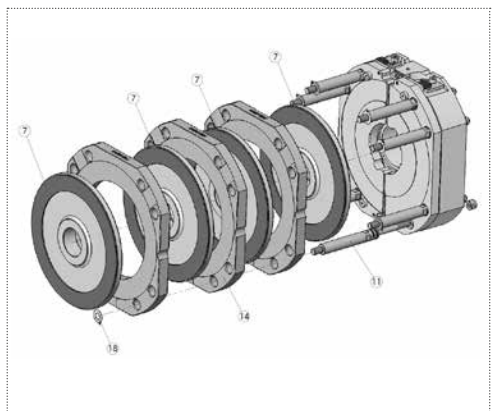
Explosionszeichnung der Bremse DFX1.
